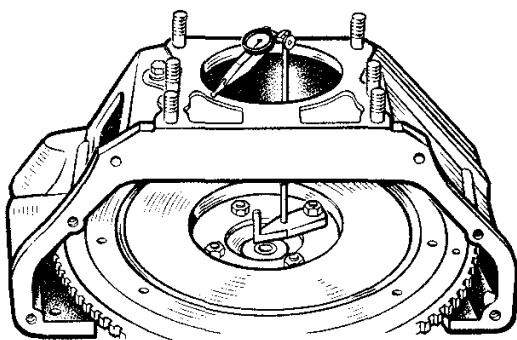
Проверка перпендикулярности заднего торца картера сцепления к оси коленчатого вала
